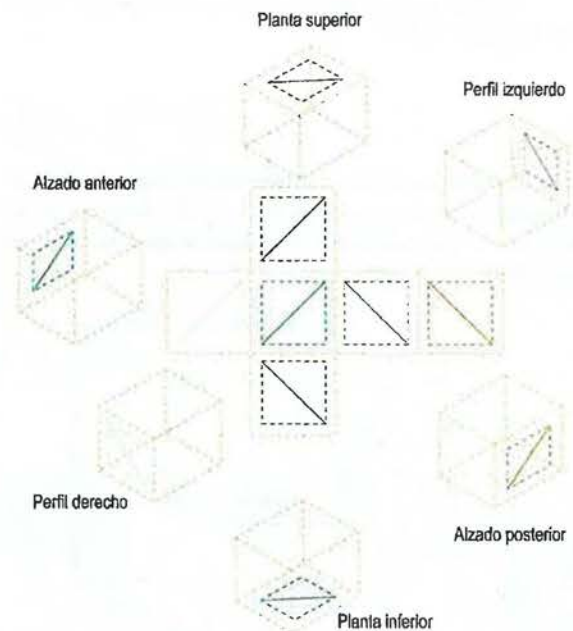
Vistas posibles de una pieza en el sistema diédrico.
